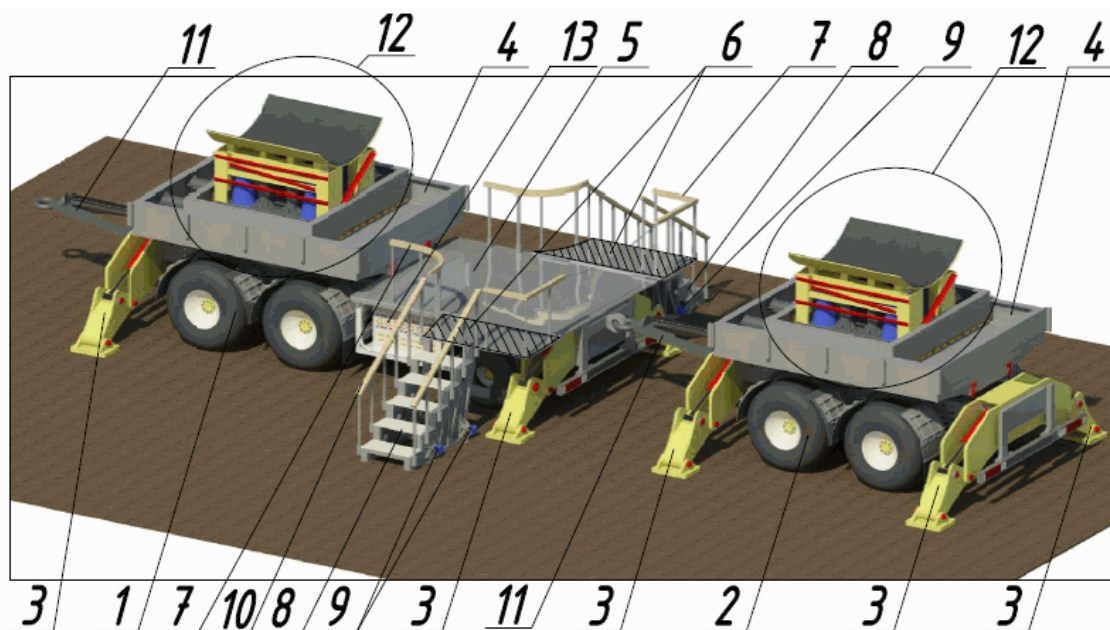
Пространственная схема предлагаемого устройства для центровки труб под сварку: 1,2 – прицепы, 3 – аутригеры, 4 – металлический
